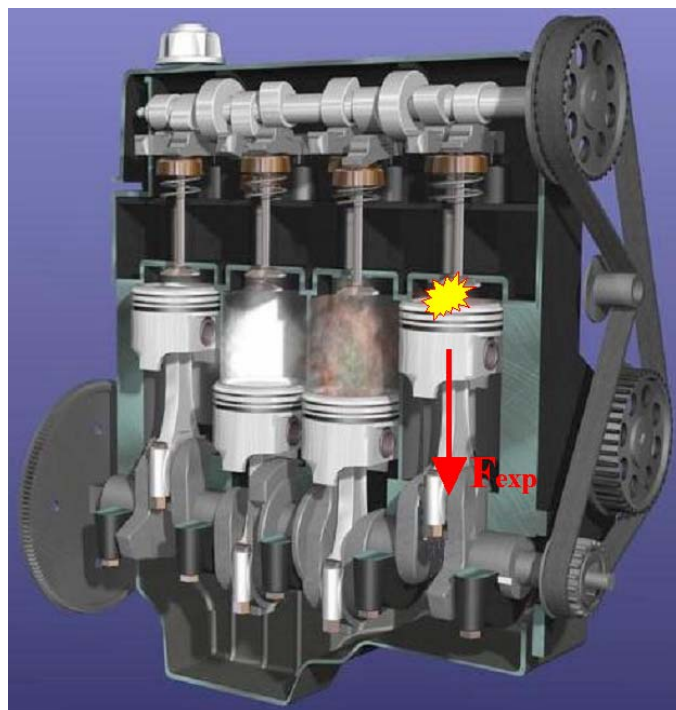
Direção da Força de Explosão " F_{exp} ".
